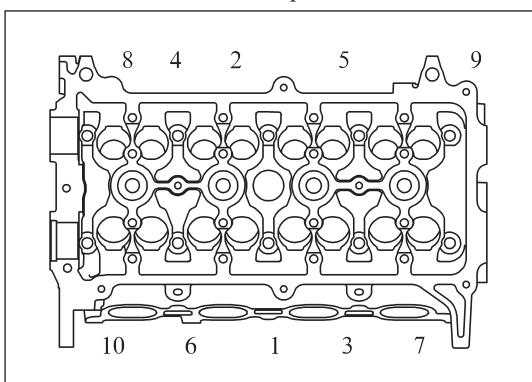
Затяжка болтов крепления головки блока цилиндров
